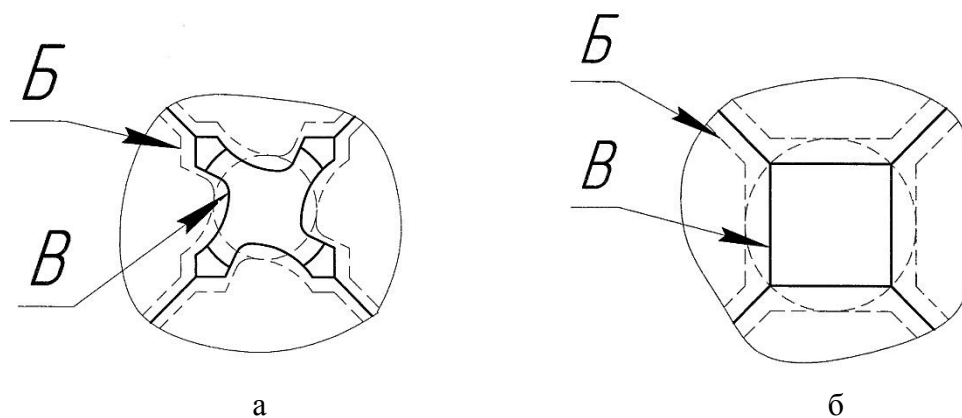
Схема формообразования рабочей части метчика (а) и хвостовой части метчика (б)
